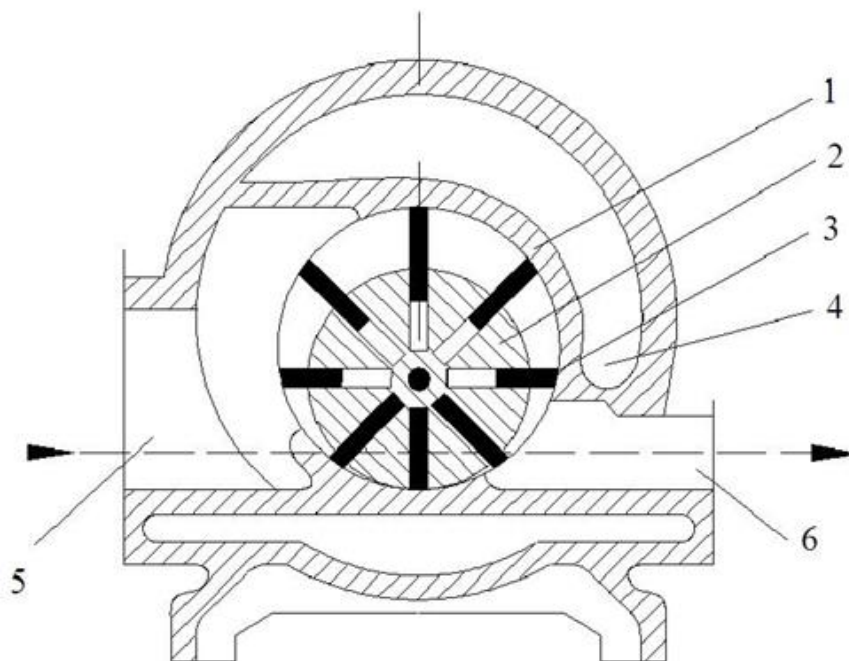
Ротаційний пластинчастий компресор: 1 - корпус; 2 - ротор; 3 - пластина; 4 - водяна сорочка; 5 - всмоктуючий патрубок; 6 - нагнітальний патрубок.
